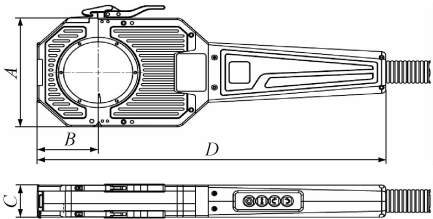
密封式全位置 TIG 管-管焊枪结构
